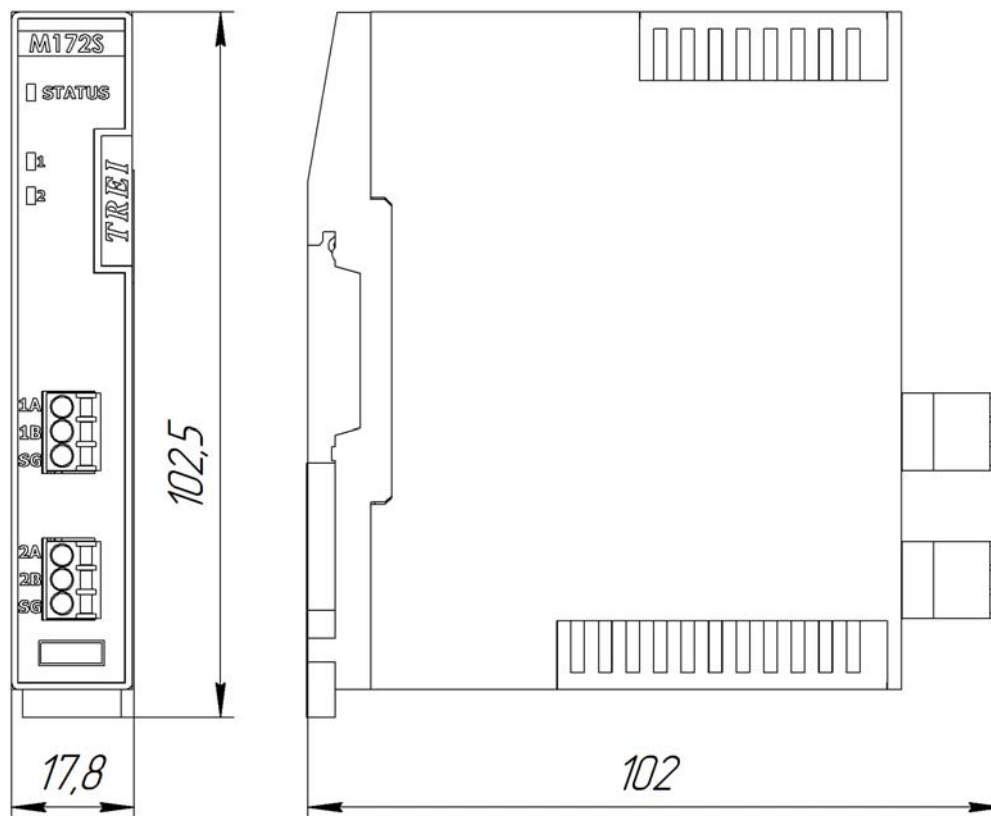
Чертеж общего вида M172S с указанием габаритных и присоединительных размеров
